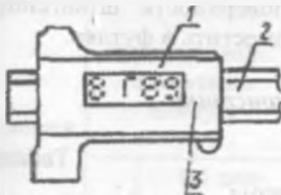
Отчетное устройство штангенциркуля. Тип ШЦЦ:
